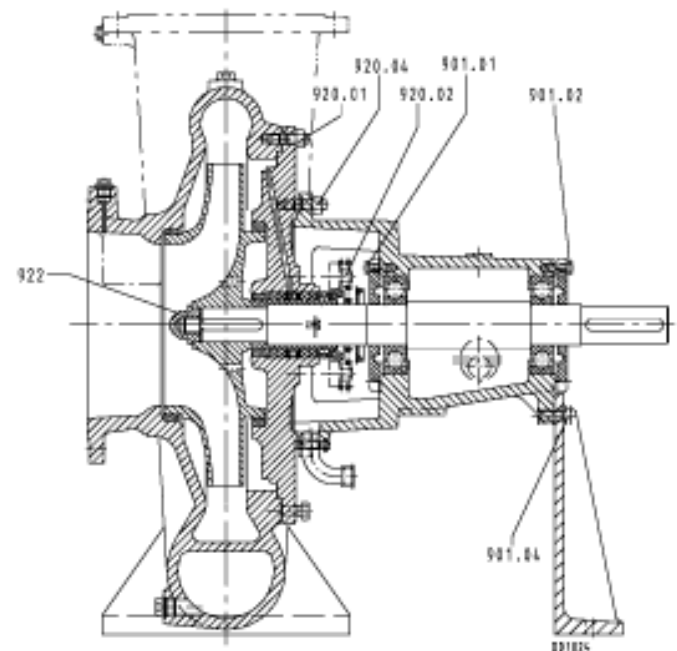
Места затяжки резьбовых соединений насоса
